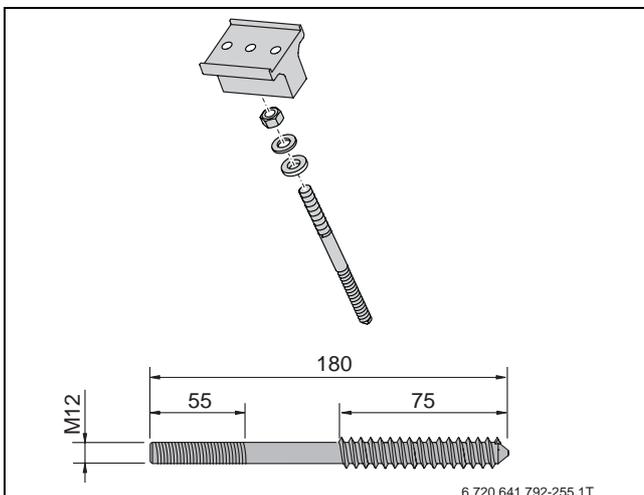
Vite prigioniera per il collegamento da tetto di pia-
